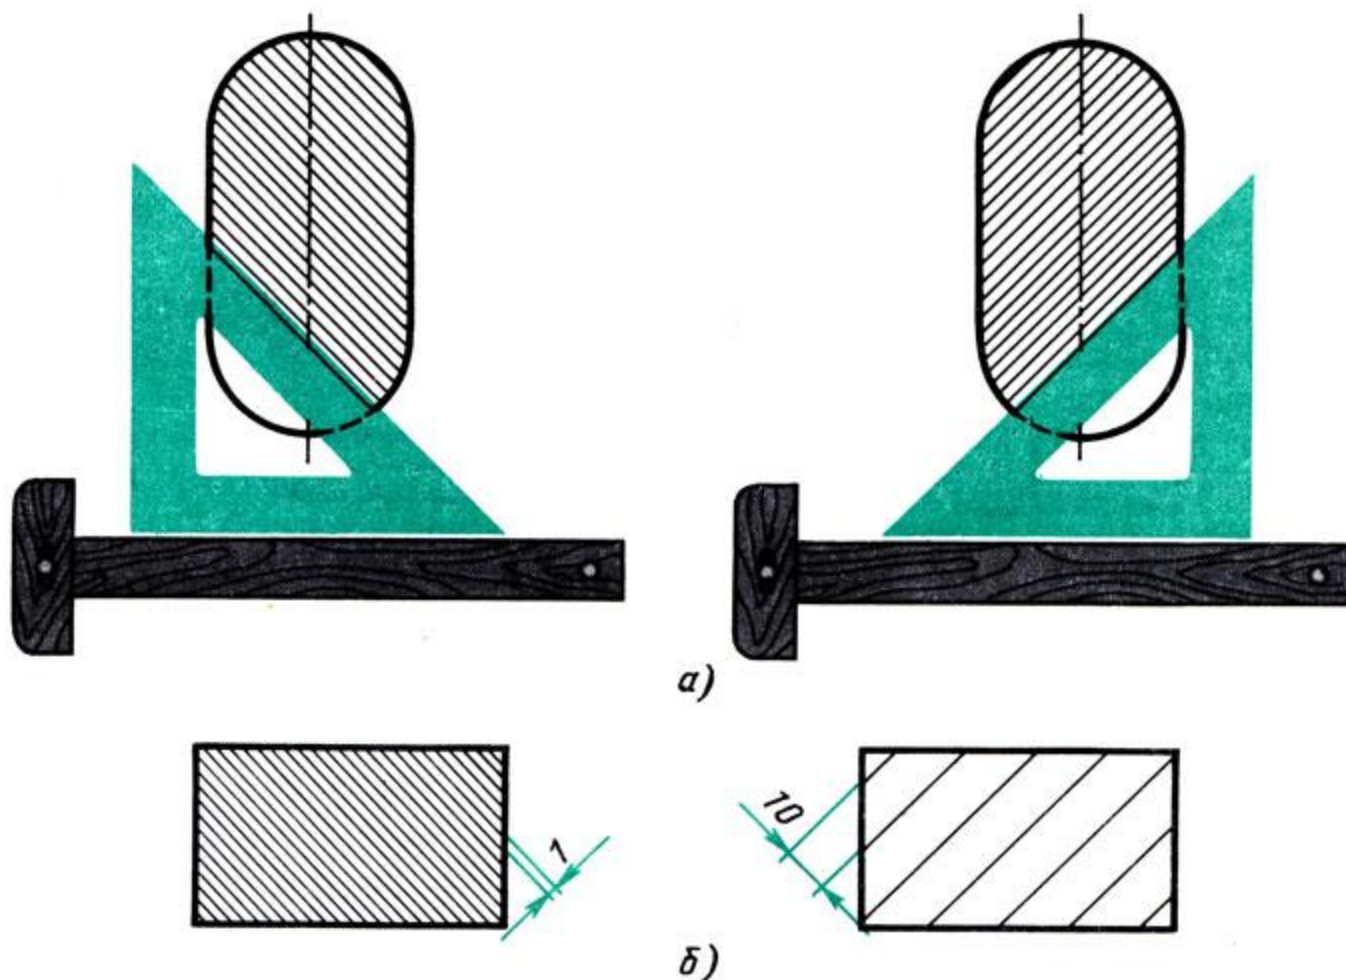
Штриховка сечений (для металлов и твердых сплавов)
